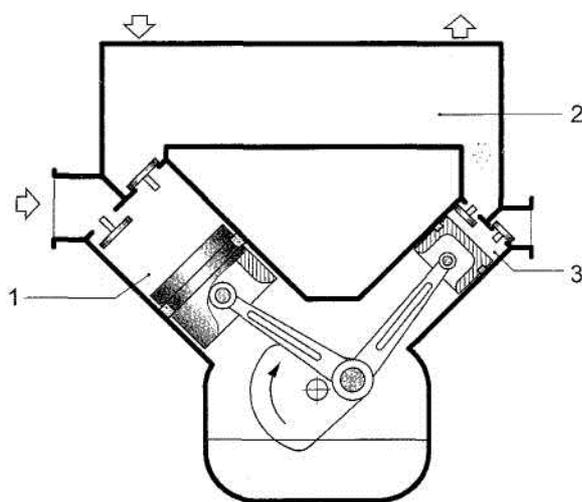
Двухступенчатый поршневой компрессор простого действия:
